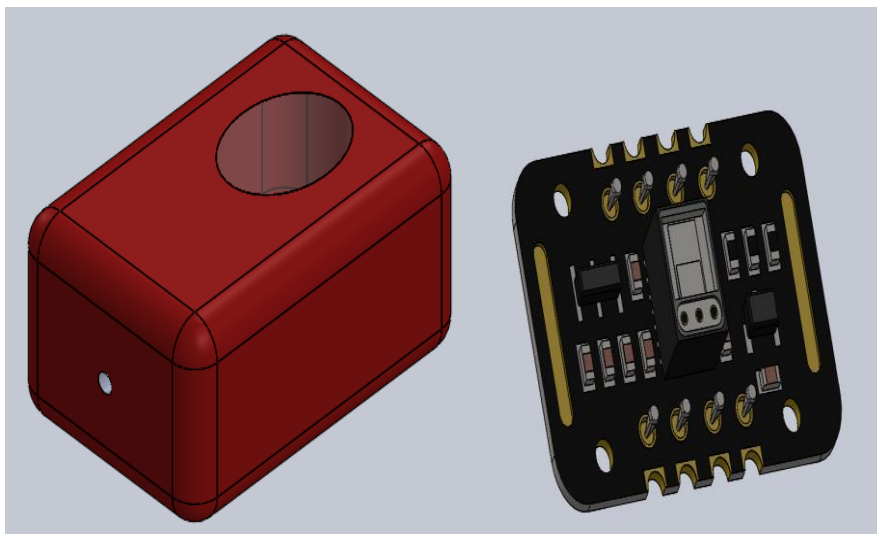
Diseño CAD del sensor MAX 30102 [autores].
